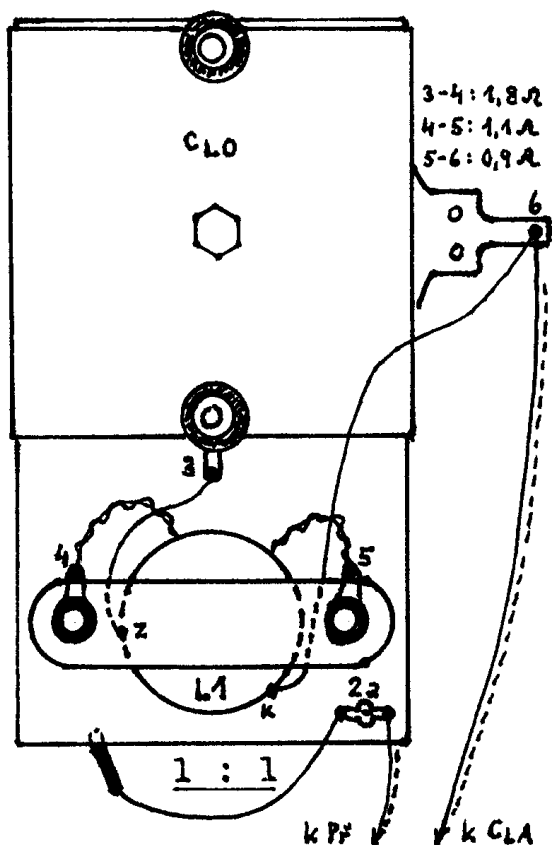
Rozložení součástí a vedení spojů v horní části skříně.
